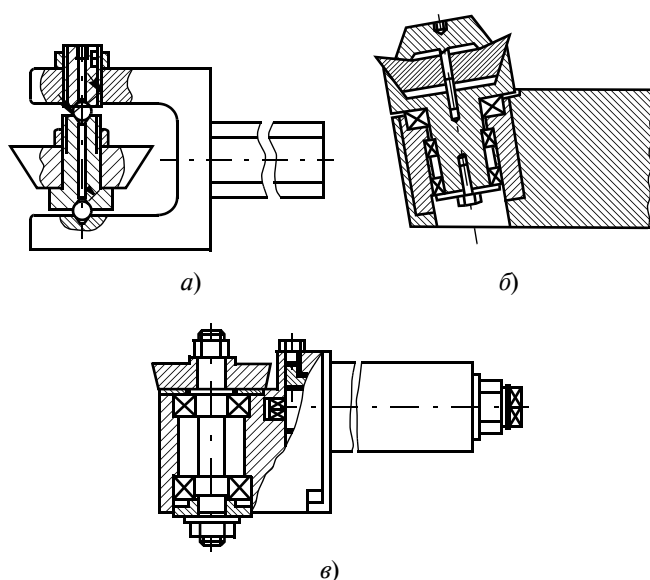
Конструкции ротационных резцов: а — ротационный самовращающийся резец [23]; б — ротационный резец [24]; в — ротационный резец [25]
